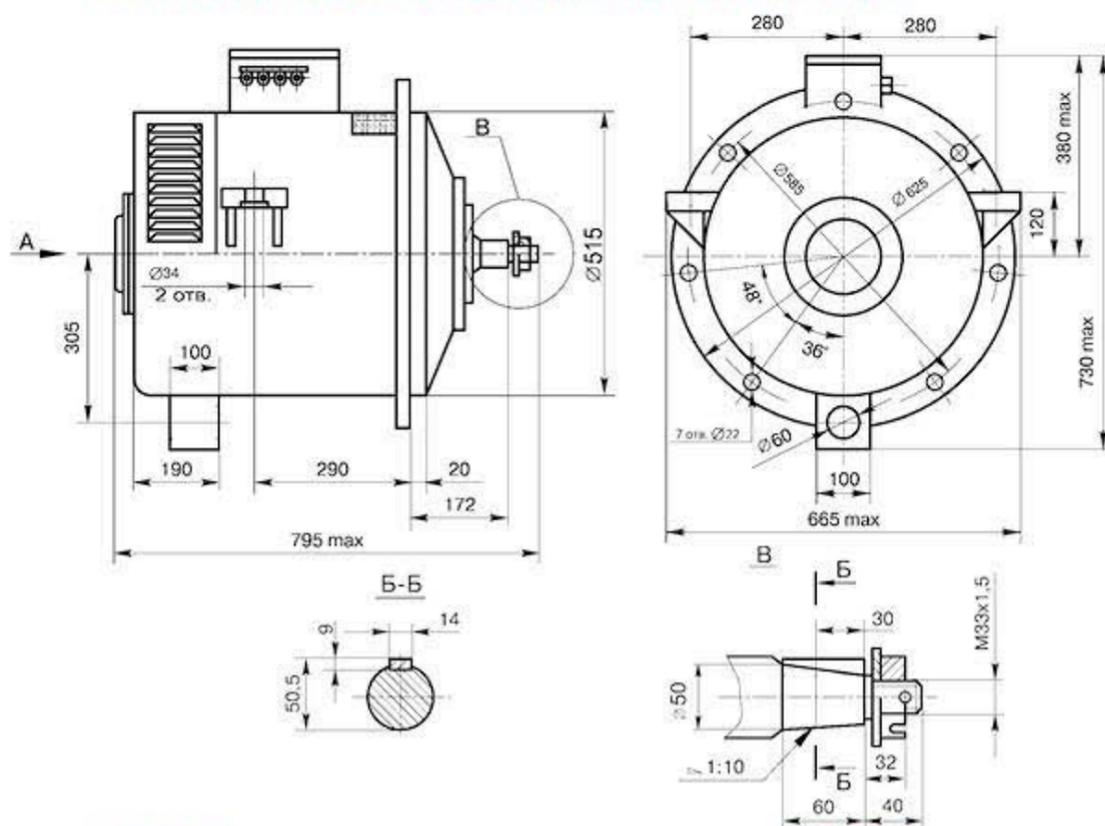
Габаритные и установочные размеры электродвигателя ДТН-45/27
